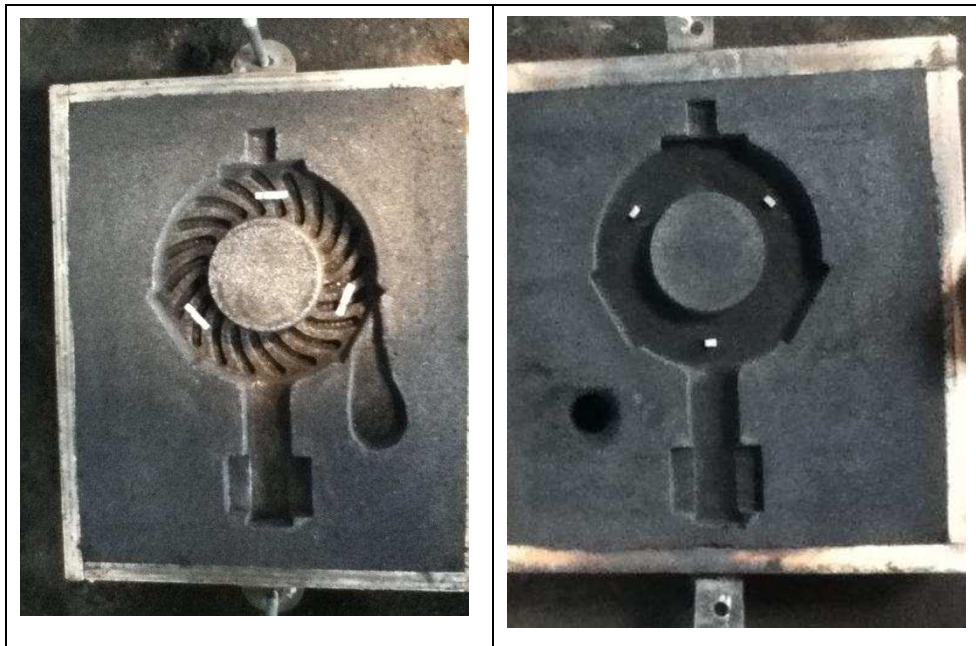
25. Montaje de los soportes en el molde del quemador A.
